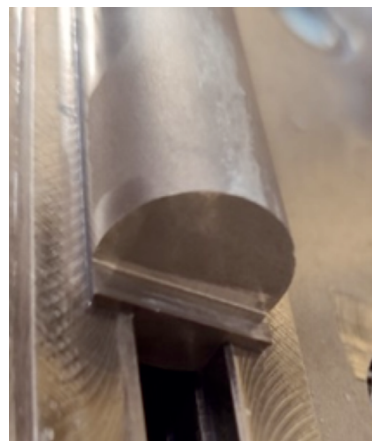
Образец заготовки из сплава Mo30TiC с технологическим хвостовиком
